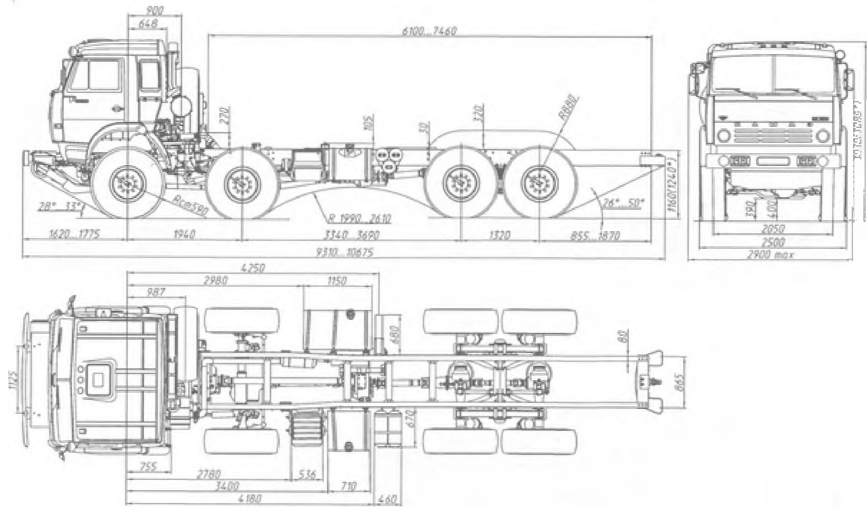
Шасси автомобиля-тягача КАМАЗ-6350. Габаритные размеры.
